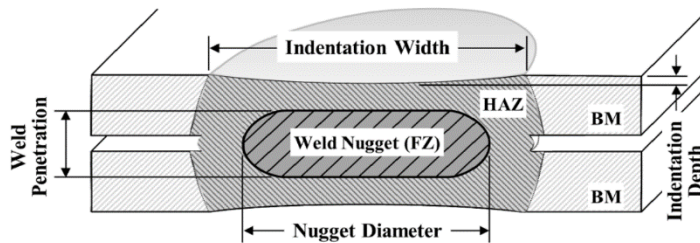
Partes de un punto de soldadura [23]
